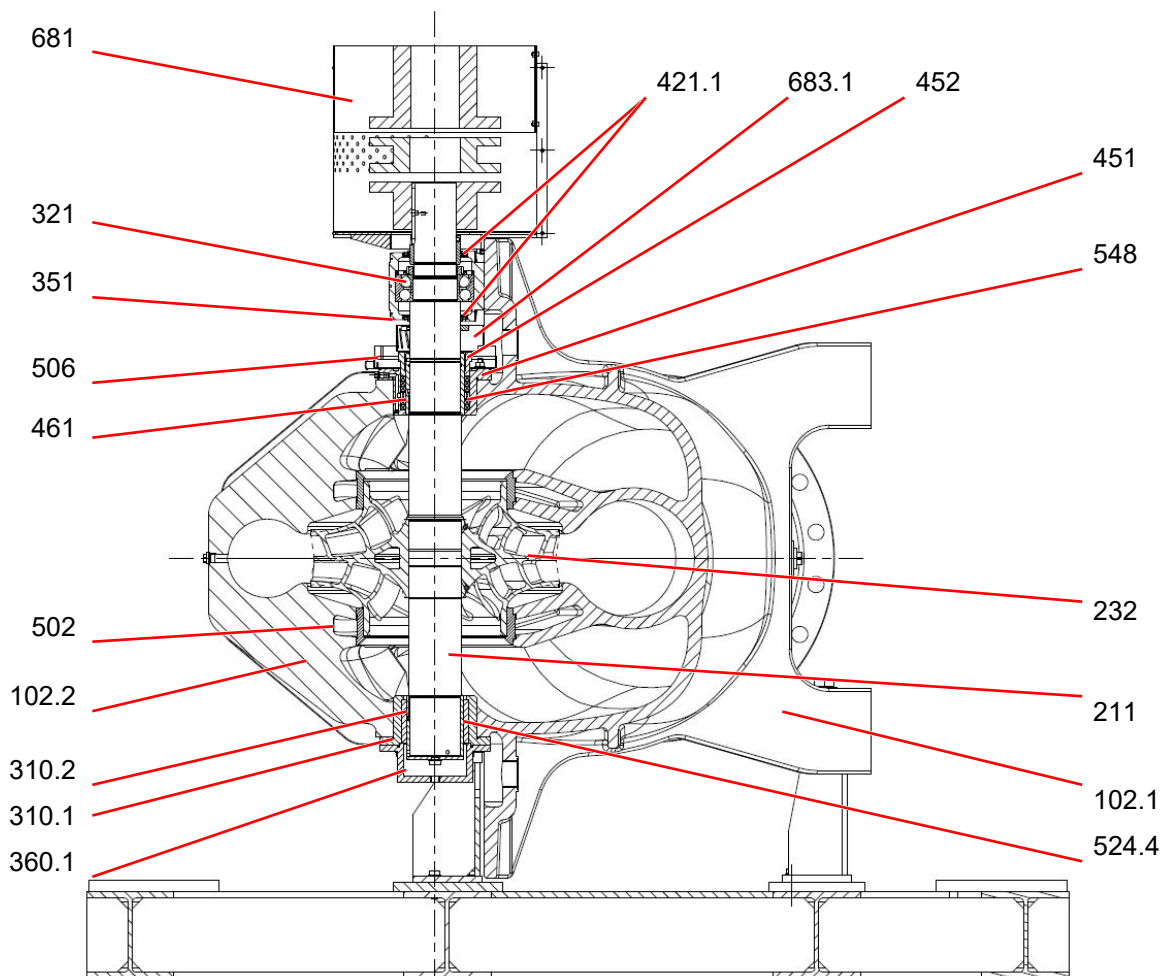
Чертеж насоса ASP-V в разрезе (соосные лопасти рабочего колеса; прессовая посадка)
